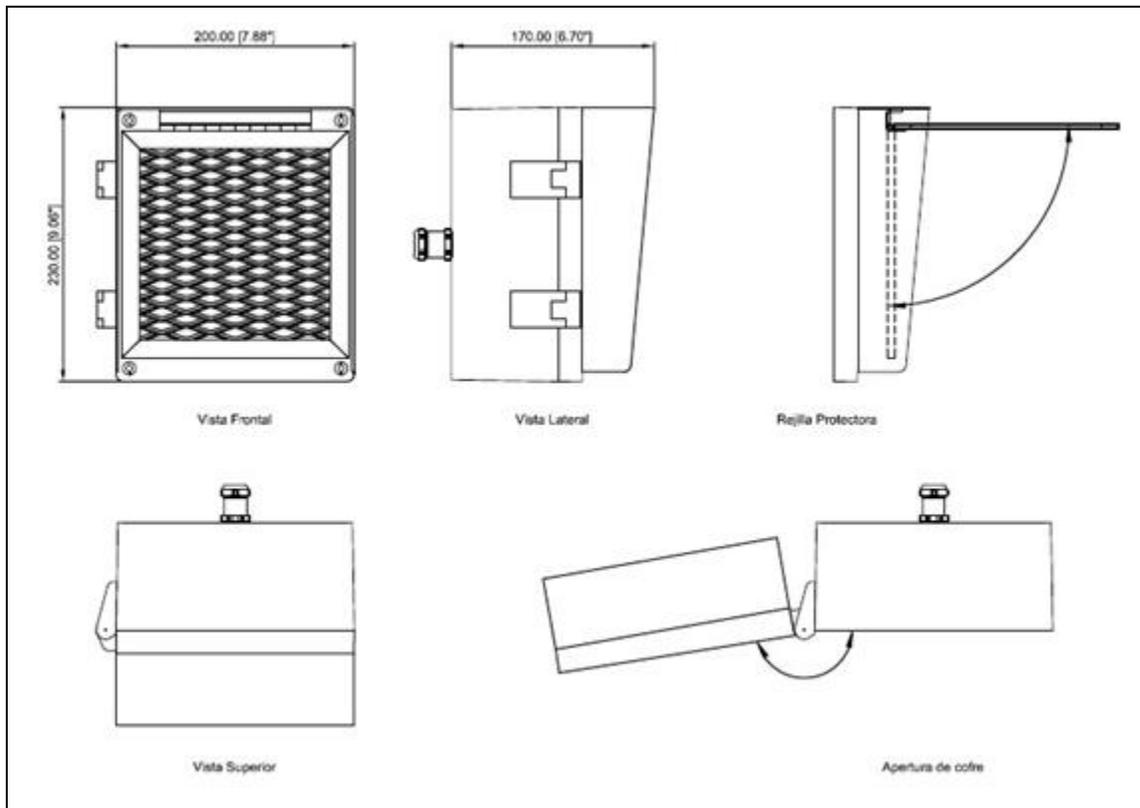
18. Cajas telefónicas que van a los soportes a muro dentro de túneles del metro. Plano realizado en AUTOCAD 2010. Archivo interno de DIMITEC.
